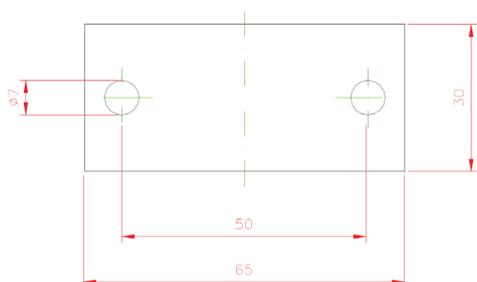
Сверлильная схема для скобы для крепления трубы
